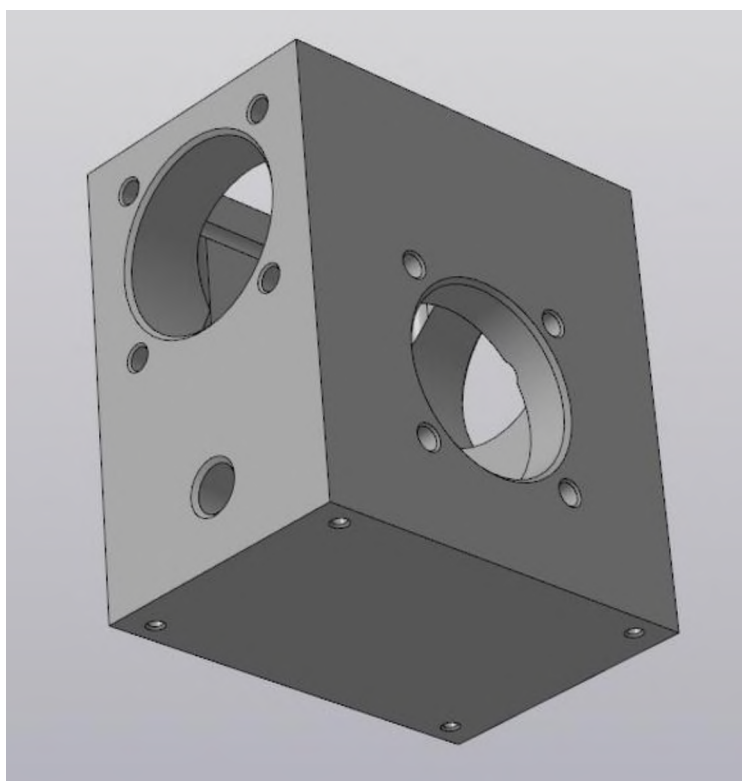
3D модель деталі «Корпус». Ізометрія, вигляд знизу
